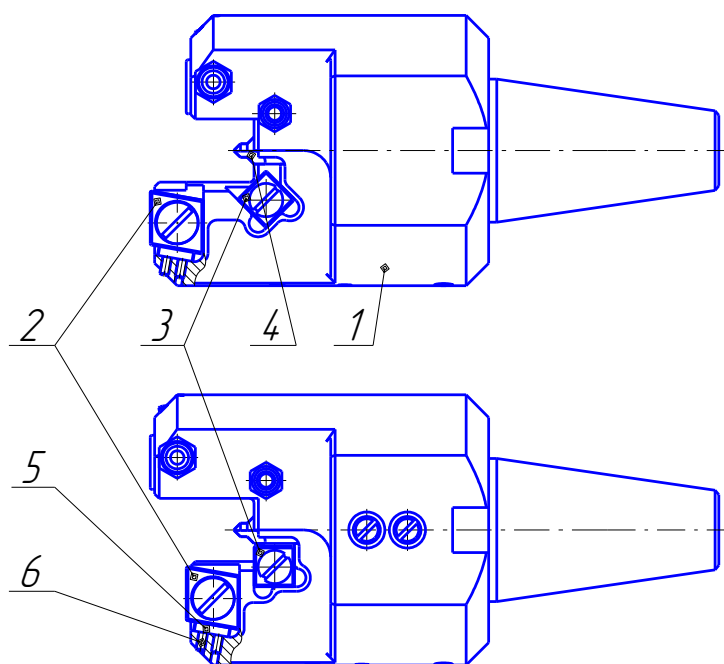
Спеціальна інструментальна головка для попередньої обробки деталі «Хрестовина»
